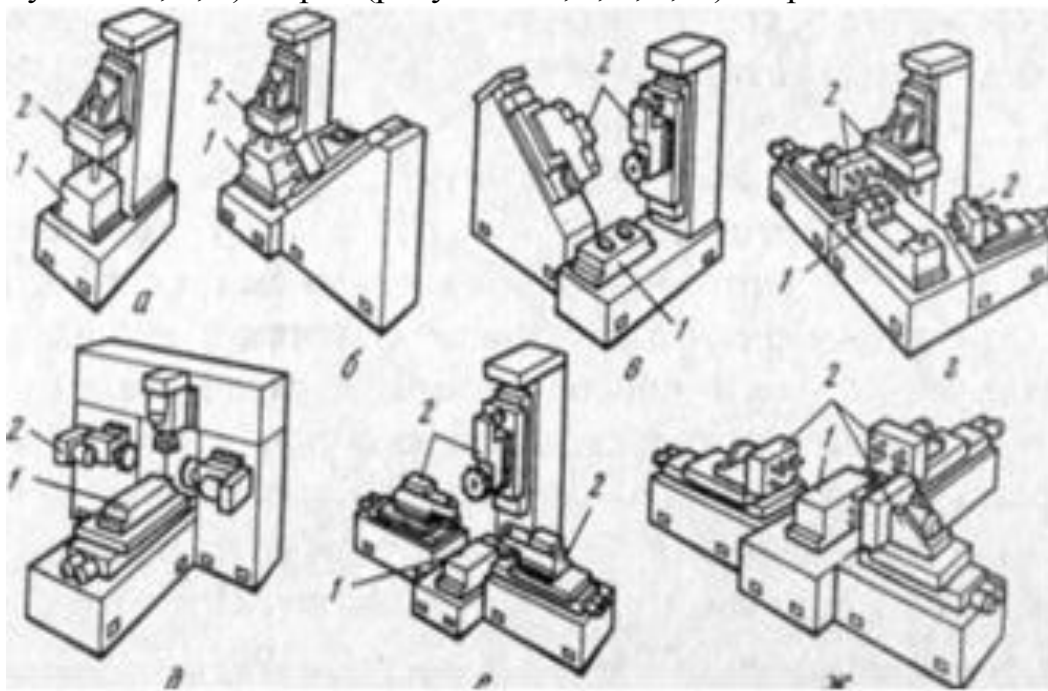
Типовые компоновки агрегатных станков со стационарными приспособлениями.
